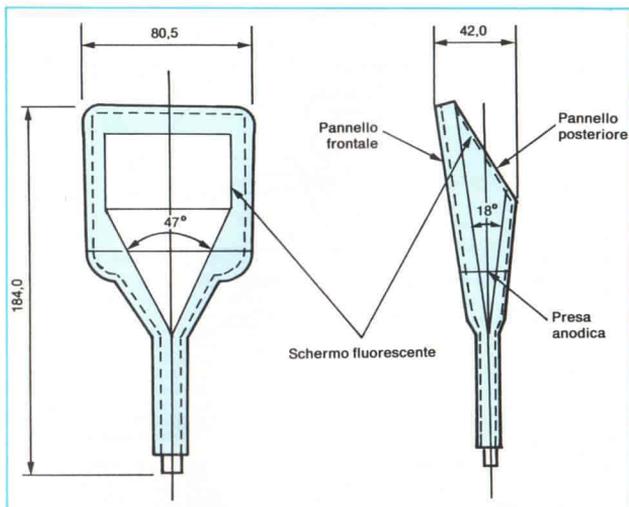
Struttura e dimensioni del tubo a colori a schermo piatto "Sun Flat".
